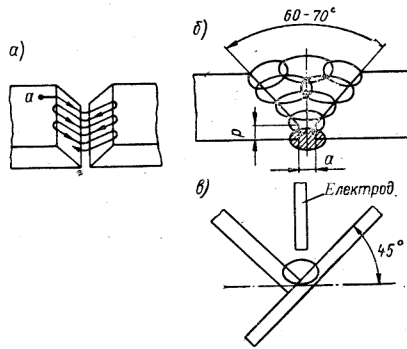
Рух електроду (а). Схеми зварювання: багат шарове (б); зварювання в "човник" (в)
